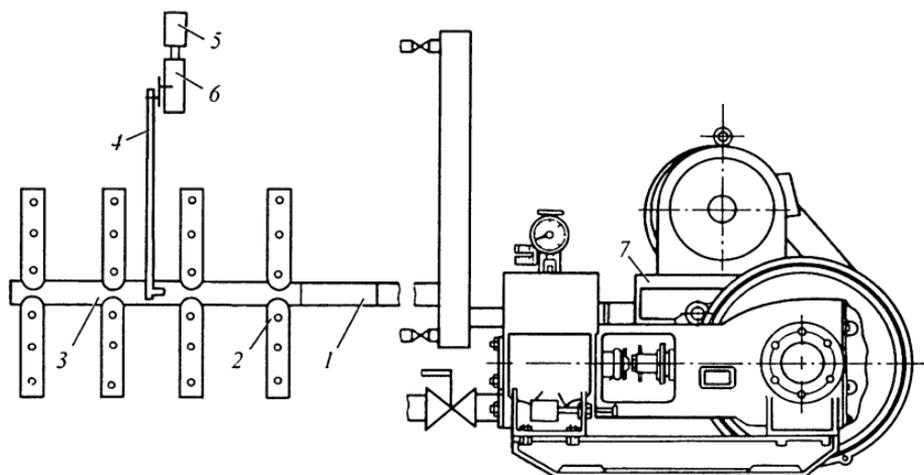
Устройство для мойки днища автомобиля с автоматическим управлением: 1 — гибкий шланг; 2 — сопла; 3 — коллектор; 4 — тяга; 5 — электроприбор; 6 — вибратор; 7 — насосная станция
